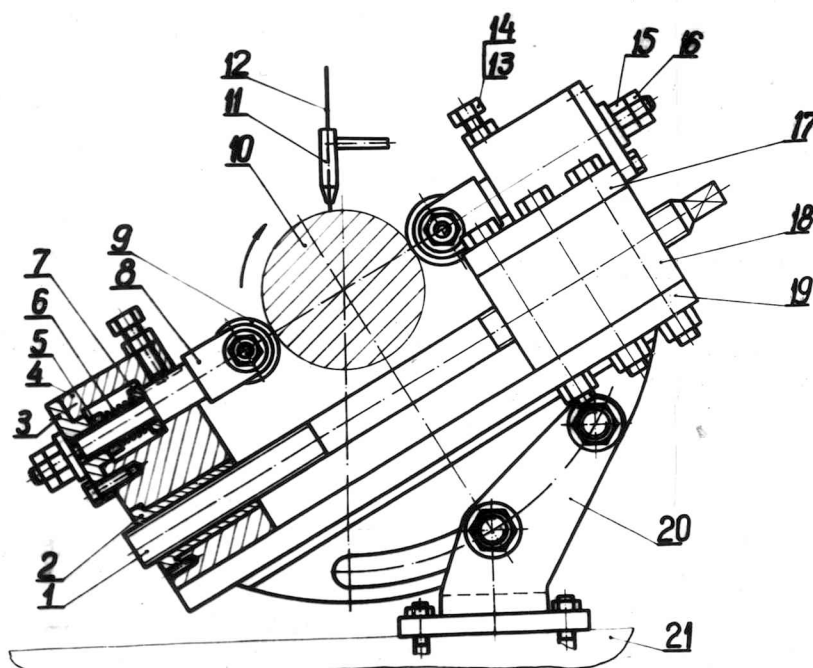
Пристосування для пластичного деформування наплавленого металу.
